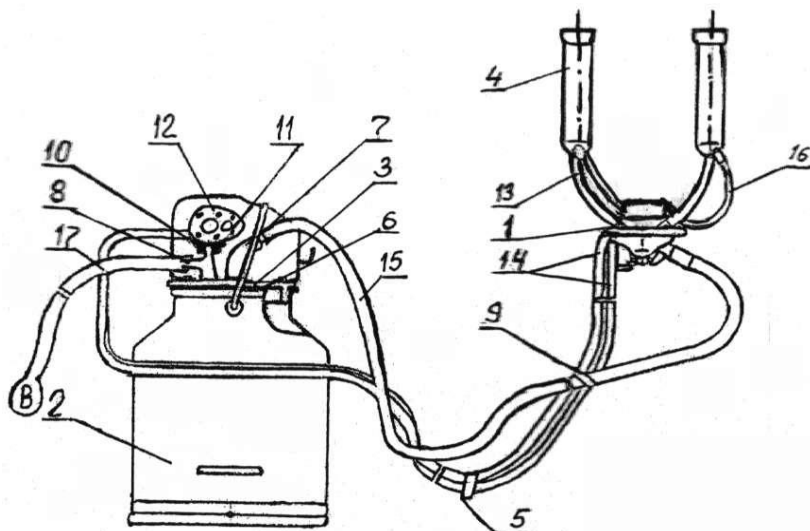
Аппарат доильный попарного доения АДС-25А.00.000, АДС-25А.00.000-01: 1 – коллектор; 2 – ведро доильное; 3 – крышка; 4 – стакан доильный; 5, 9 – кольца; 6 – прокладка; 7, 8 – патрубок; 10 – адаптер; 11 – втулка; 12 – пульсатор попарного доения L80; 13 – молочная трубка; 14 – шланг резиновый диаметром 7 мм переменного вакуума; 15 – шланг молочный ПВХ диаметром 14 мм; 16 – мультишланг; 17 – шланг резиновый диаметром 11 мм постоянного вакуума.
